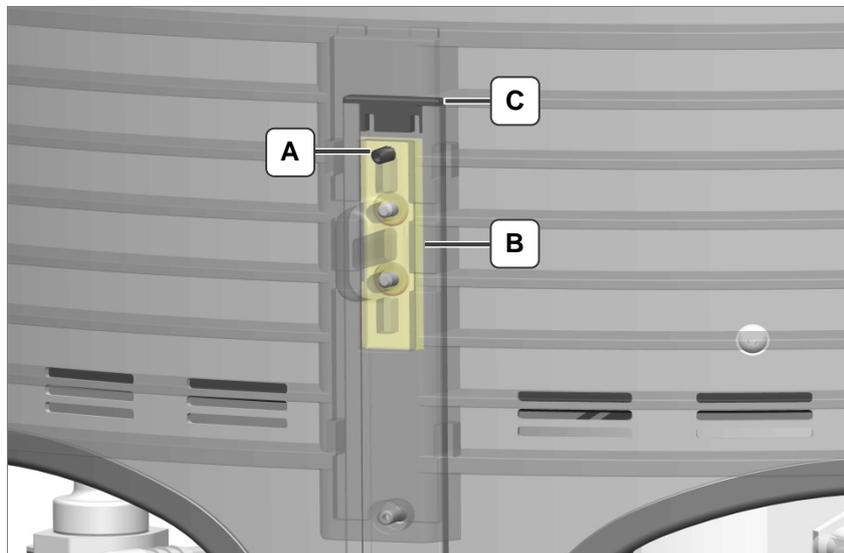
Mécanisme de guidage des grilles de protection
